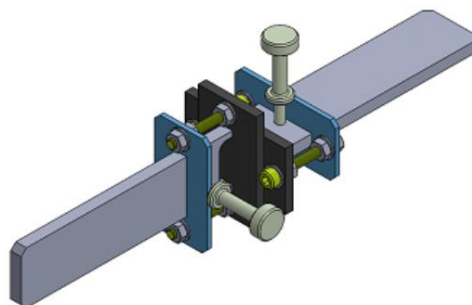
Приспособление для испытания прочности сварного шва
